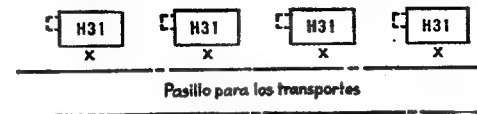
Disposición corriente de máquinas. El material se traslada de una máquina a otra cargado sobre bandejas móviles, que se llevan mediante carretillas mecánicas. Un pasillo permite el acceso a cada máquina.
